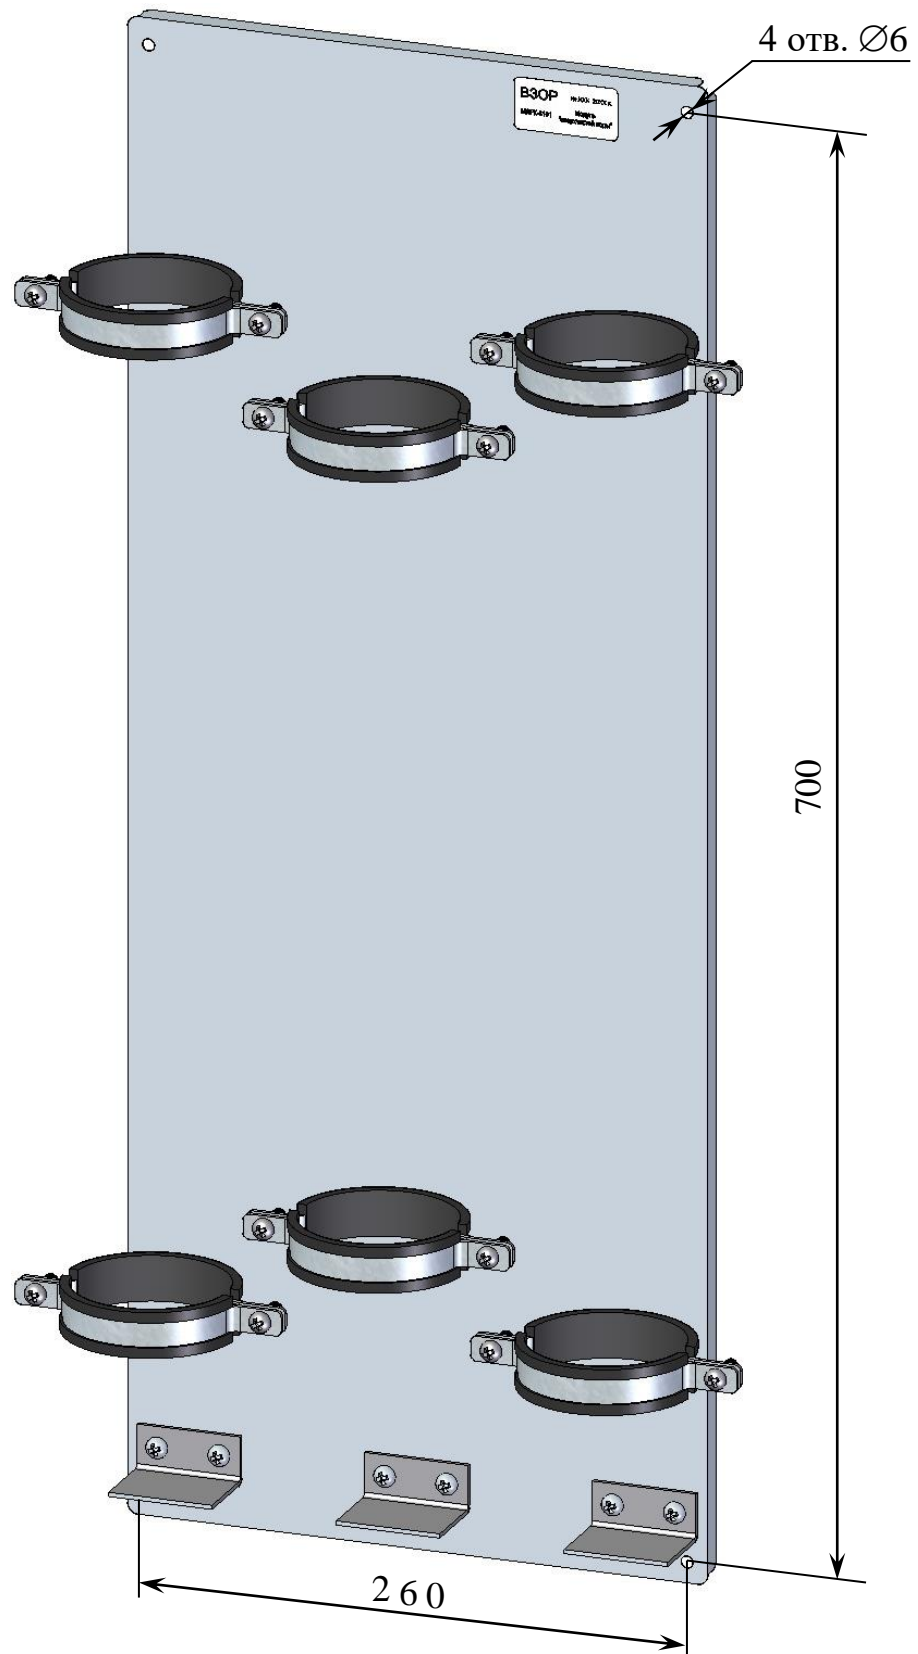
Расположение и размер отверстий для крепления панели модуля
